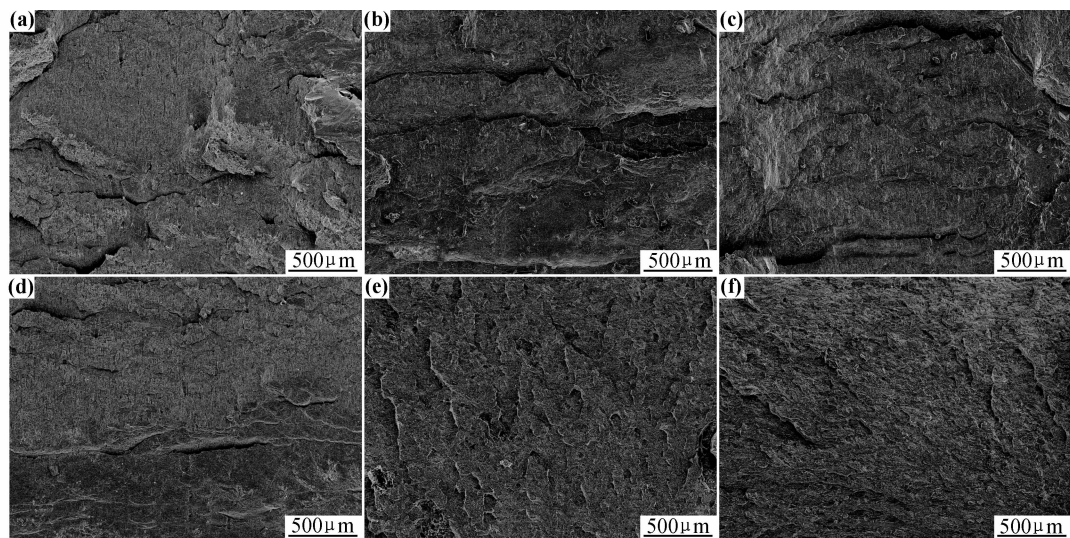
焊接接头低倍断口形貌及其断裂模式
